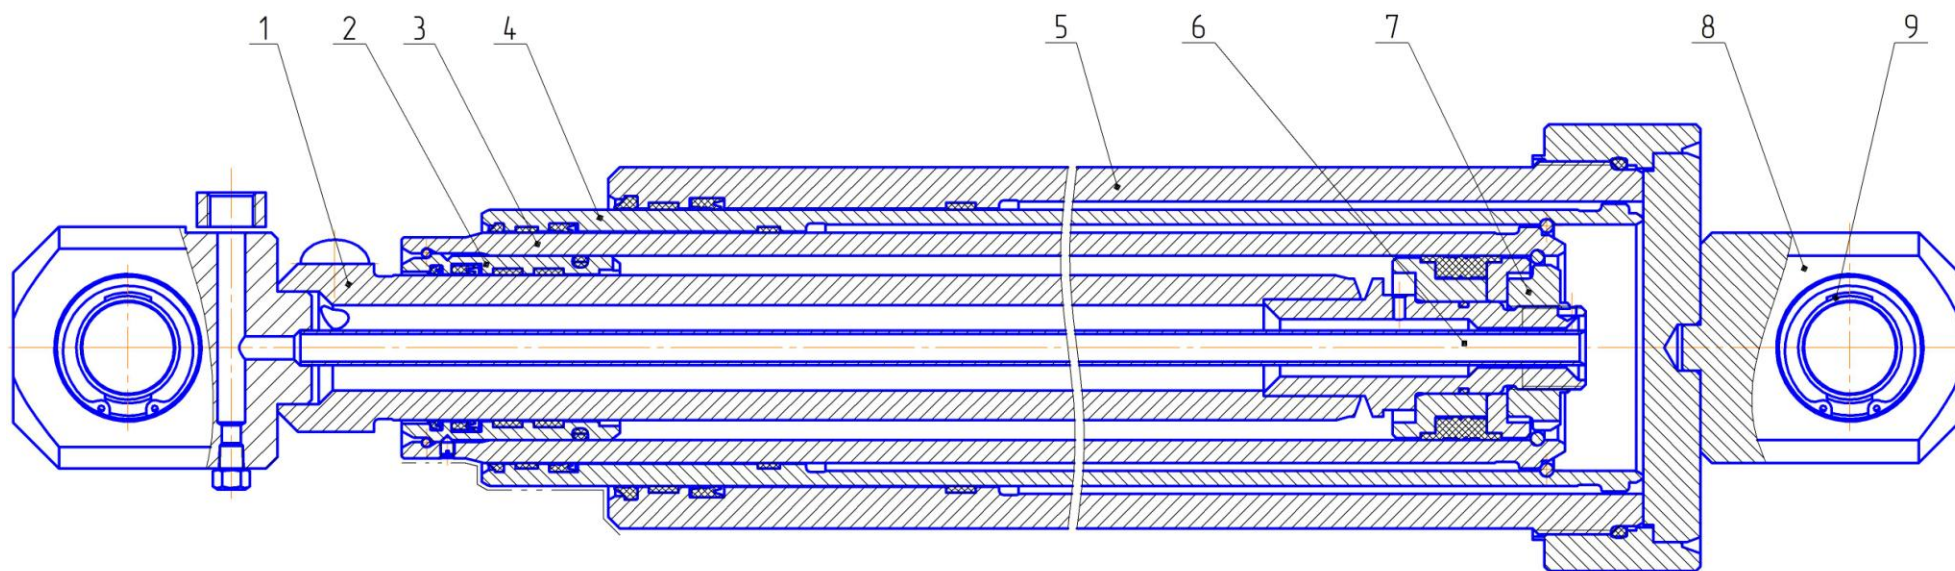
Гидроцилиндр телескопический (для мусоровоза КО-456-20.)
